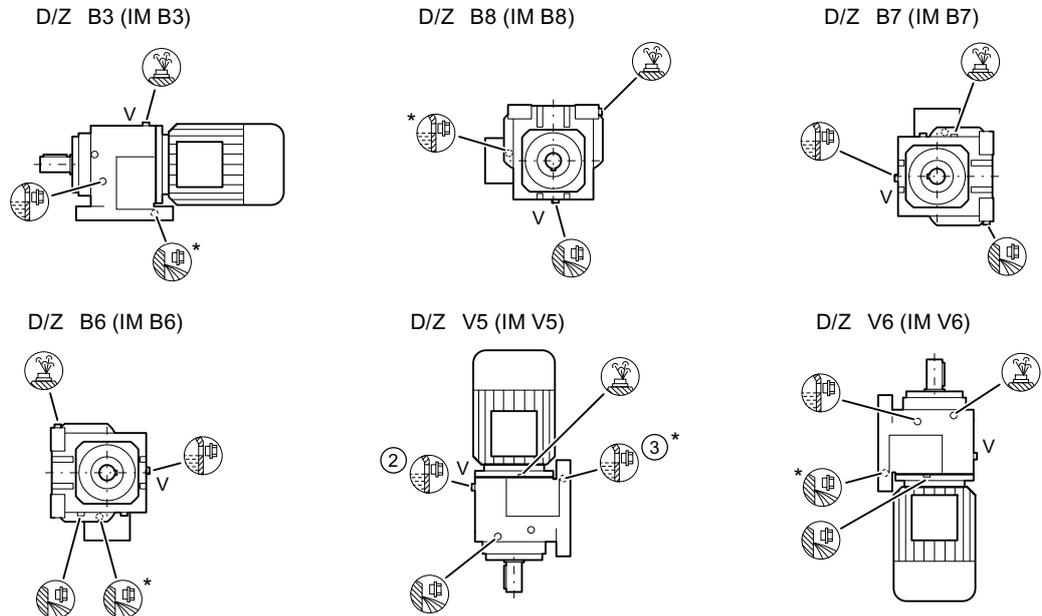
Formes de construction pour D/Z, tailles 18 - 88
